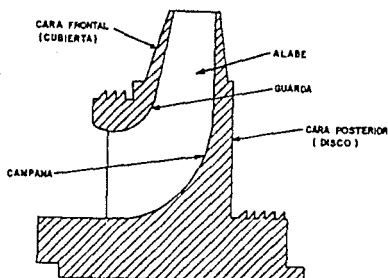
PARTES DEL IMPULSOR DE UN COMPRESOR CENTRÍFUGO
